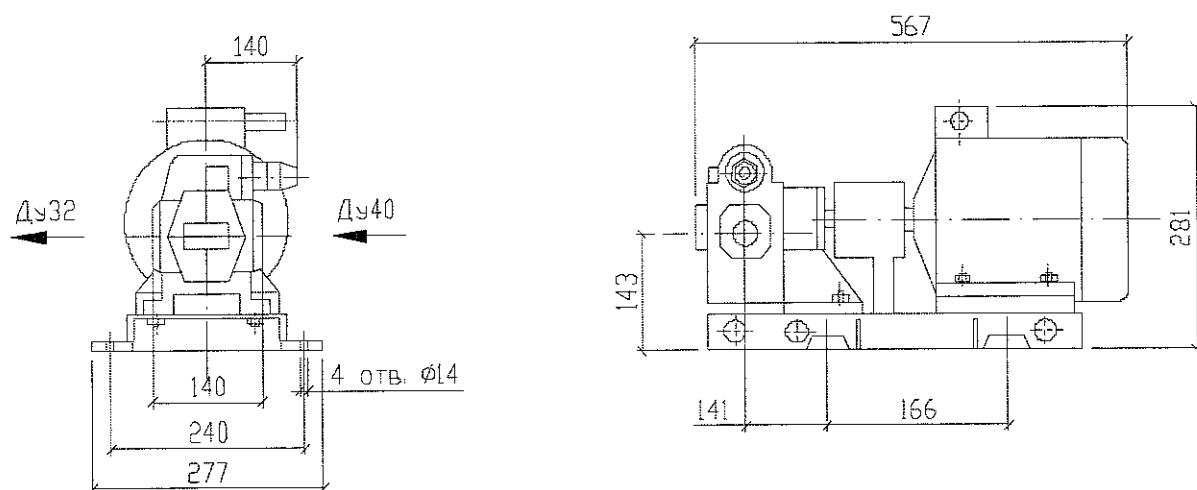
Габаритный чертеж насоса пополнения
